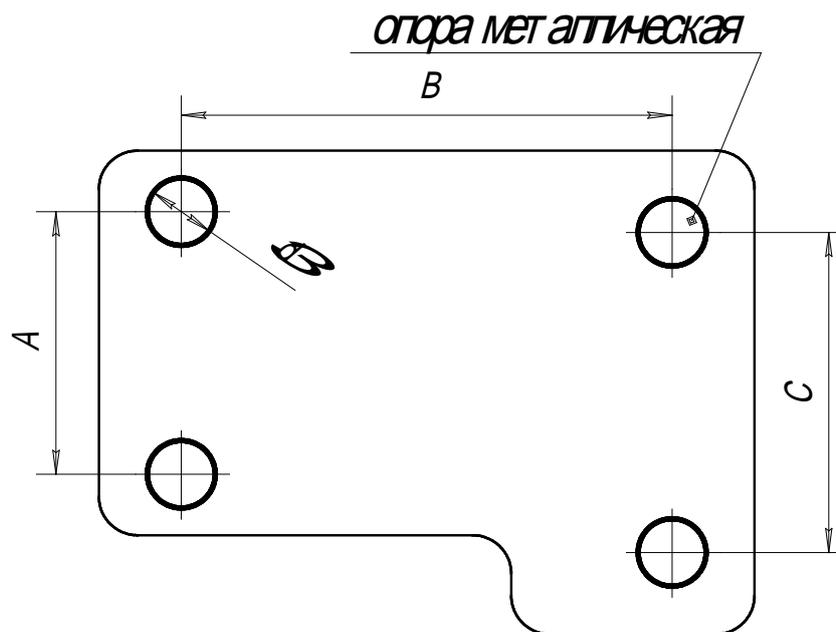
Схема расстановки опор зубофрезерного станка модели 5K801
